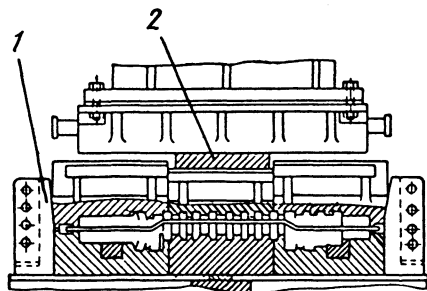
Трехсекционный штамп для штамповки поковки по частям
